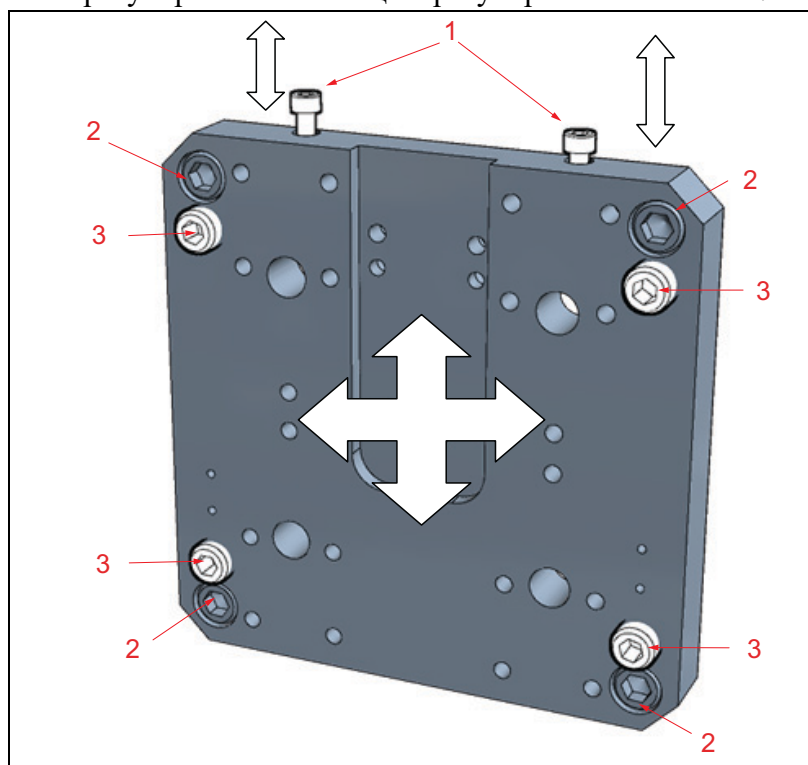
Монтажная пластина фрезерной головки и точки регулировки
